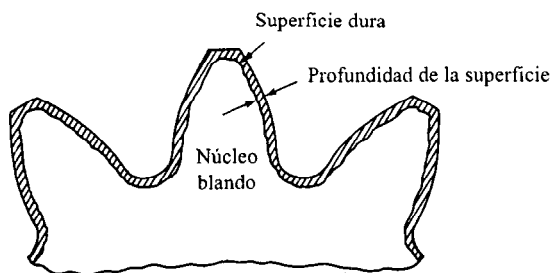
Sección de diente de engrane endurecido en la superficie
